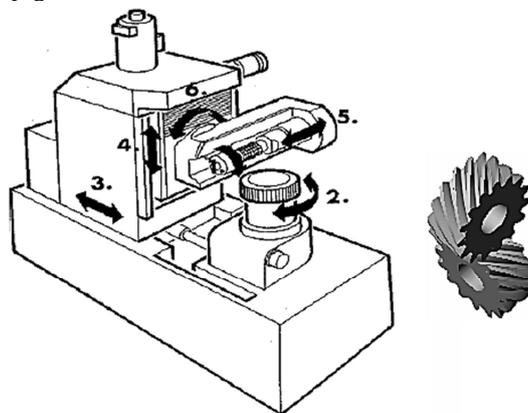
Schéma d'une machine à tailler les engrenages [13]
